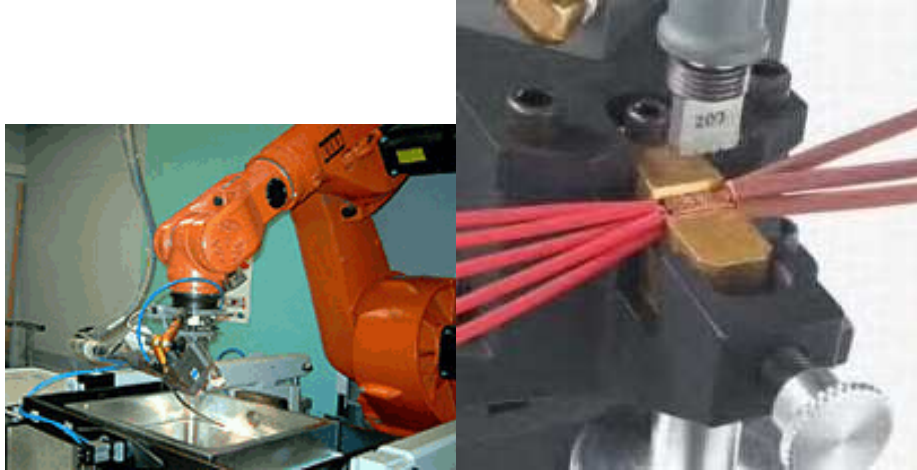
888 Soldadura Ultrasónica
